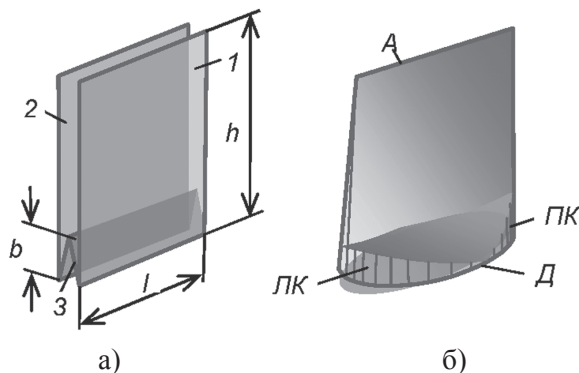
Пакування з гнучкого матеріалу: конструкція заготовки (а); форма засобу пакування (б)
